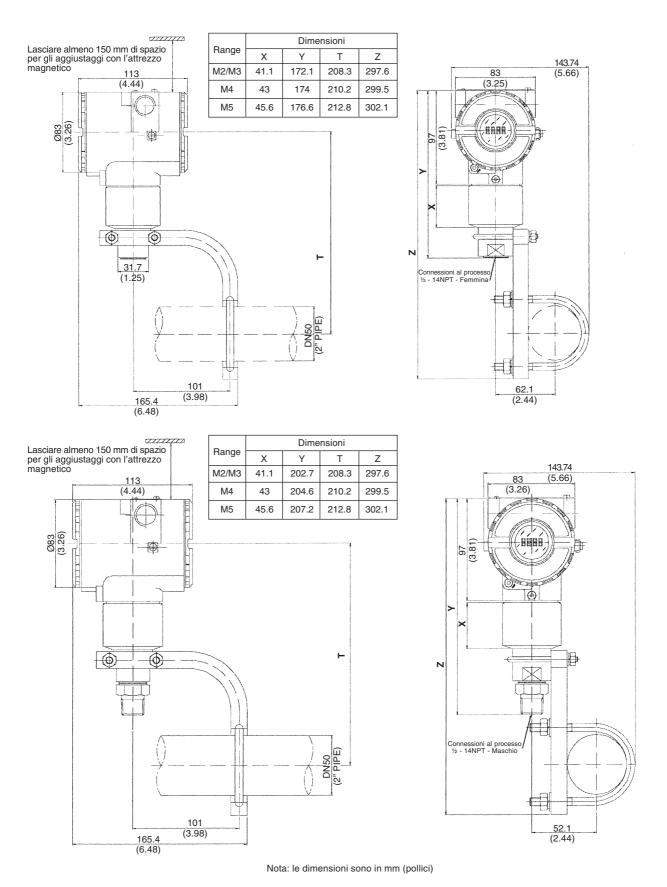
A - Dimensioni di ingombro e posizioni di montaggio per il trasmettitore LD291.
